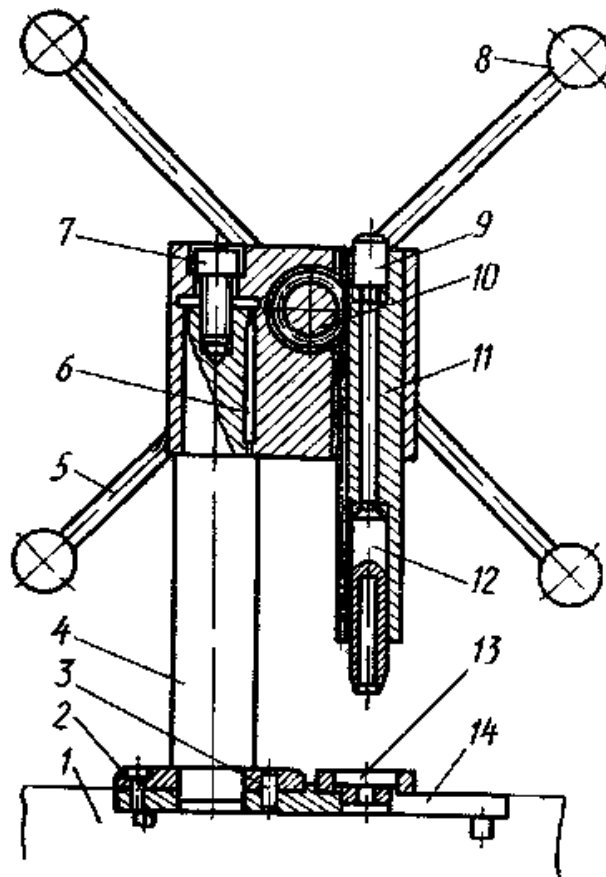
Універсальний пристрій УПРС-1: 1 – стіл; 2 – гвинт; 3 – штифт;
